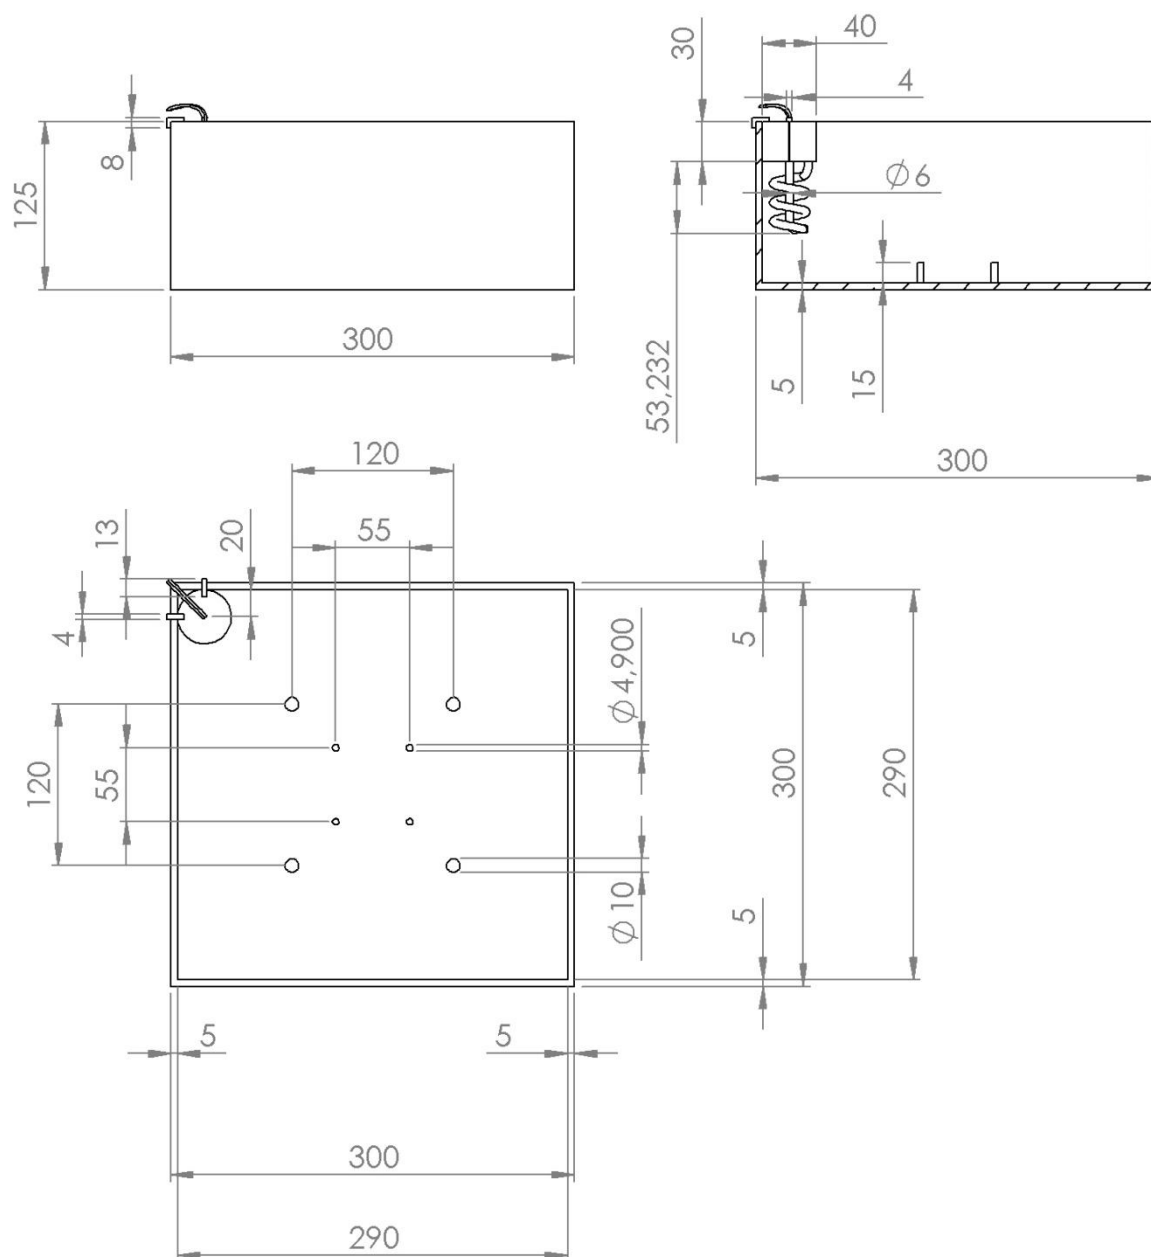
Technische tekeningen van de gehele meetopstelling, met de klok mee: vooraanzicht, zijaanzicht en bovenaanzicht. Alle maten zijn in millimeter.
